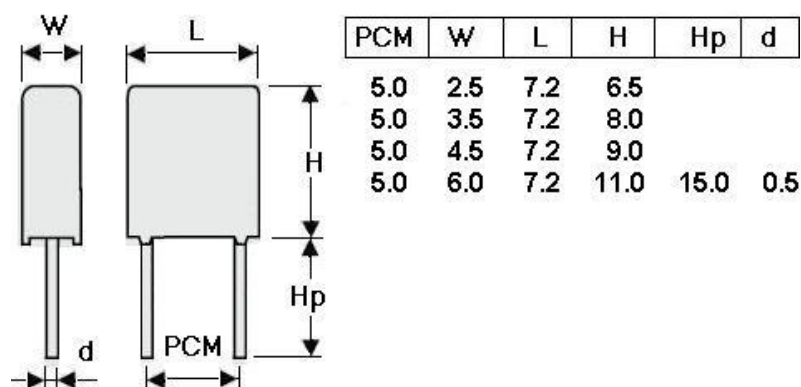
Габаритні розміри конденсатора B32529C1102J000
